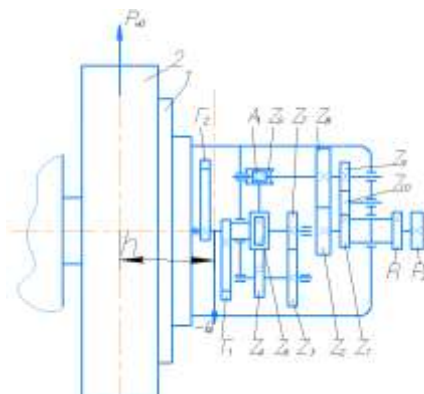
Балансирующее устройство шлифовального станка с ручным приводом
